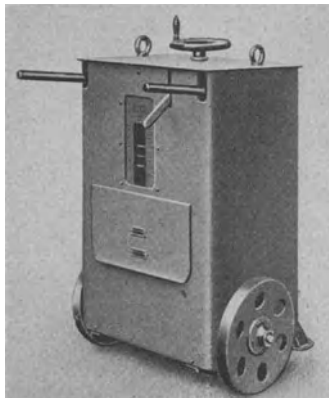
Fahrbarer Schweißumspanner mit Luftkühlung.
